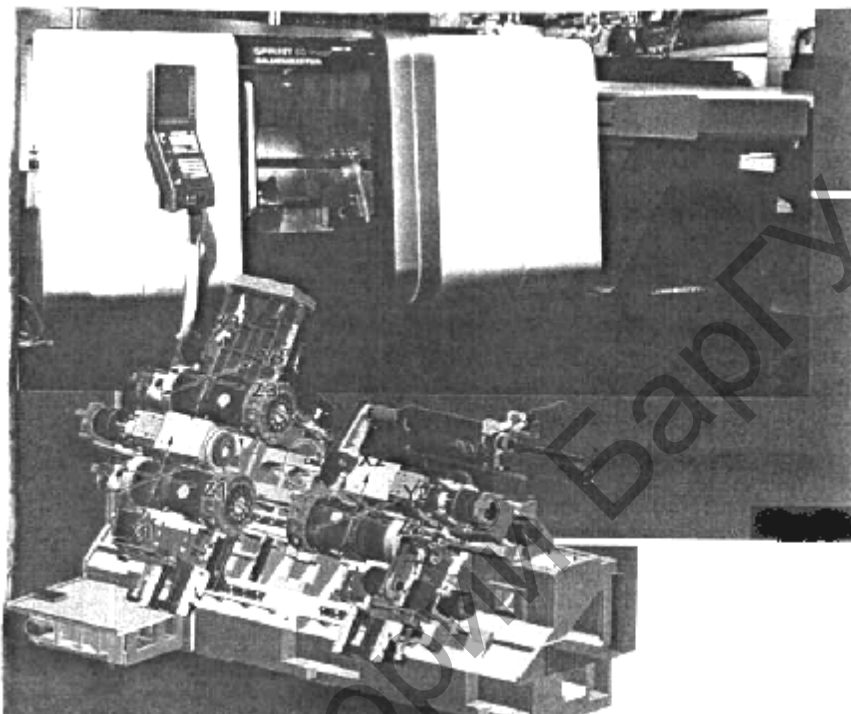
Токарный обрабатывающий центр SPRINT 50 Linear (Германия)
